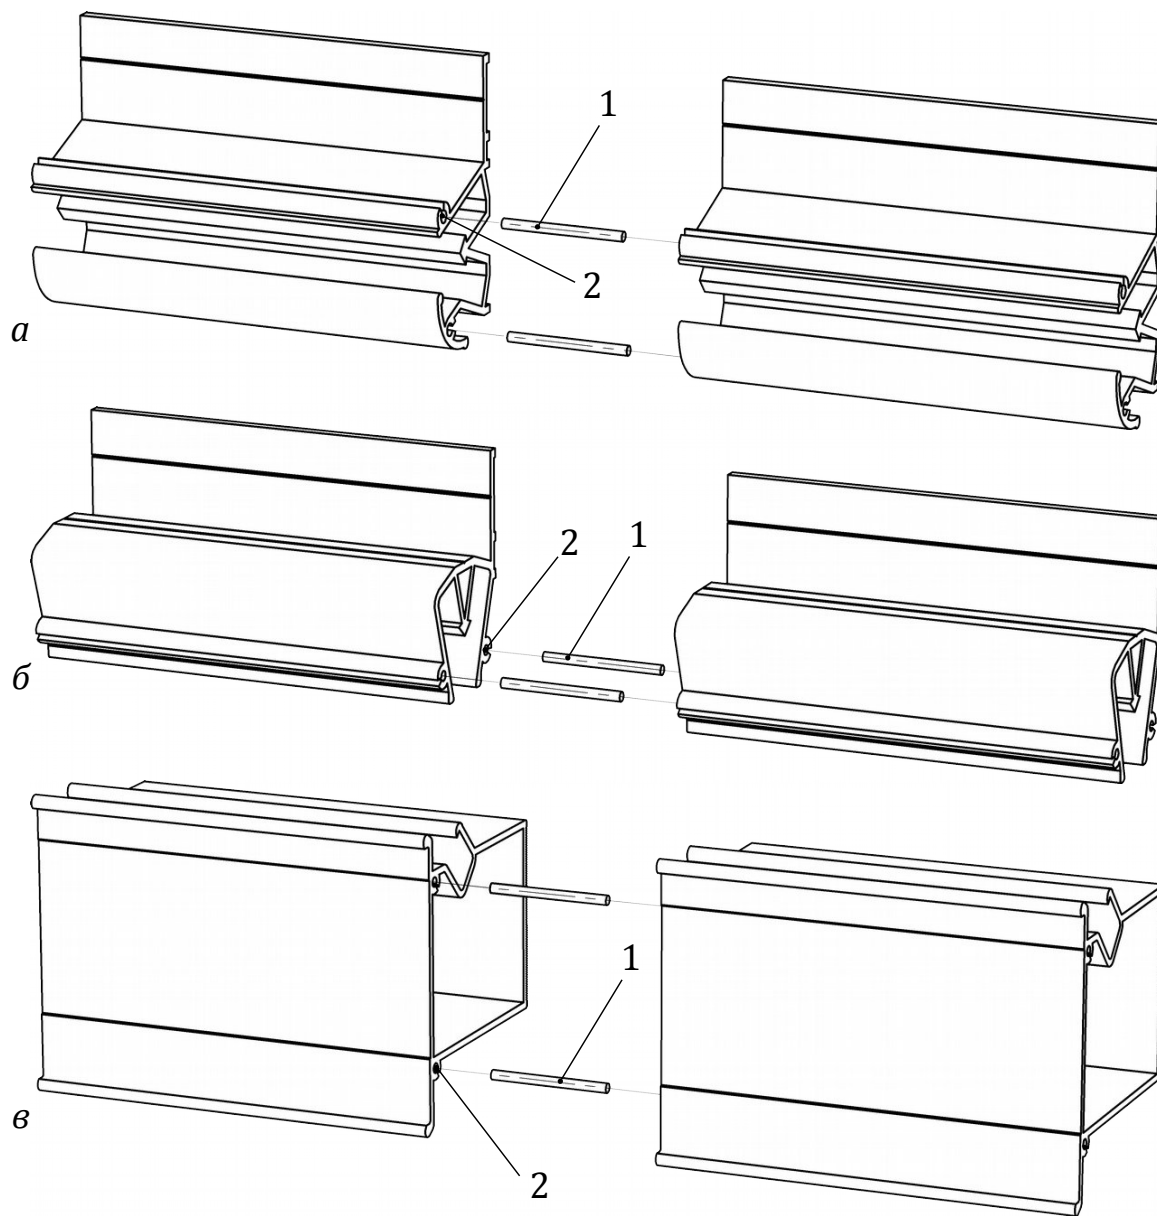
Стыковка профилей при помощи соединительных осей
